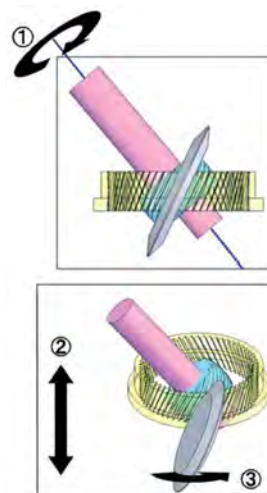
Движения и инструмент, необходимые для правки бочкообразного абразивного червяка
